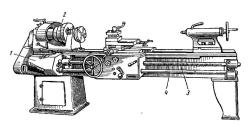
Токарно-винторезный станок со ступенчатым шкивом: I — коробка подач, 2 — ступенчатый шкив, β — ходовой винт, δ — ходовой вал
